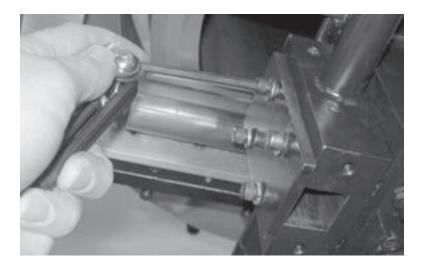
Desserrez les vis du plateau porte-outil pour monter le porte-outil sur la traverse.
